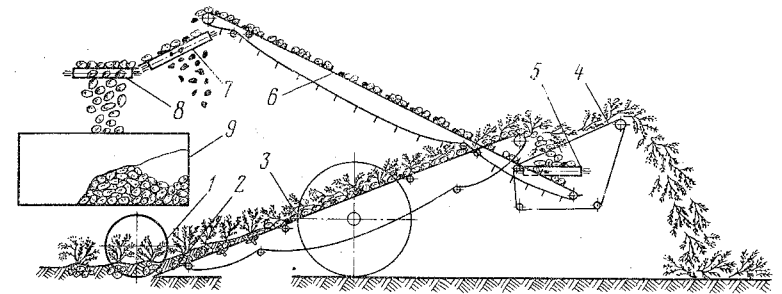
Схема комбайна «Уидсед»: 1 — диски; 2 — лемех; 3 — основной элеватор; 4 — ботвоудаляющий транспортер; 5 — поперечный транспортер; 6 — боковой элеватор; 7 — горка; 8 — транспортер-переборщик; 9 — тележка
